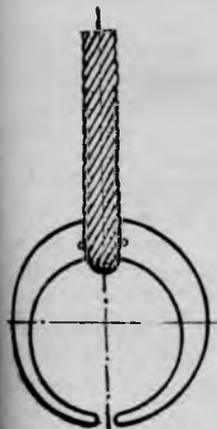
Разрезное кольцо конструкции ЦНИИМЭ
